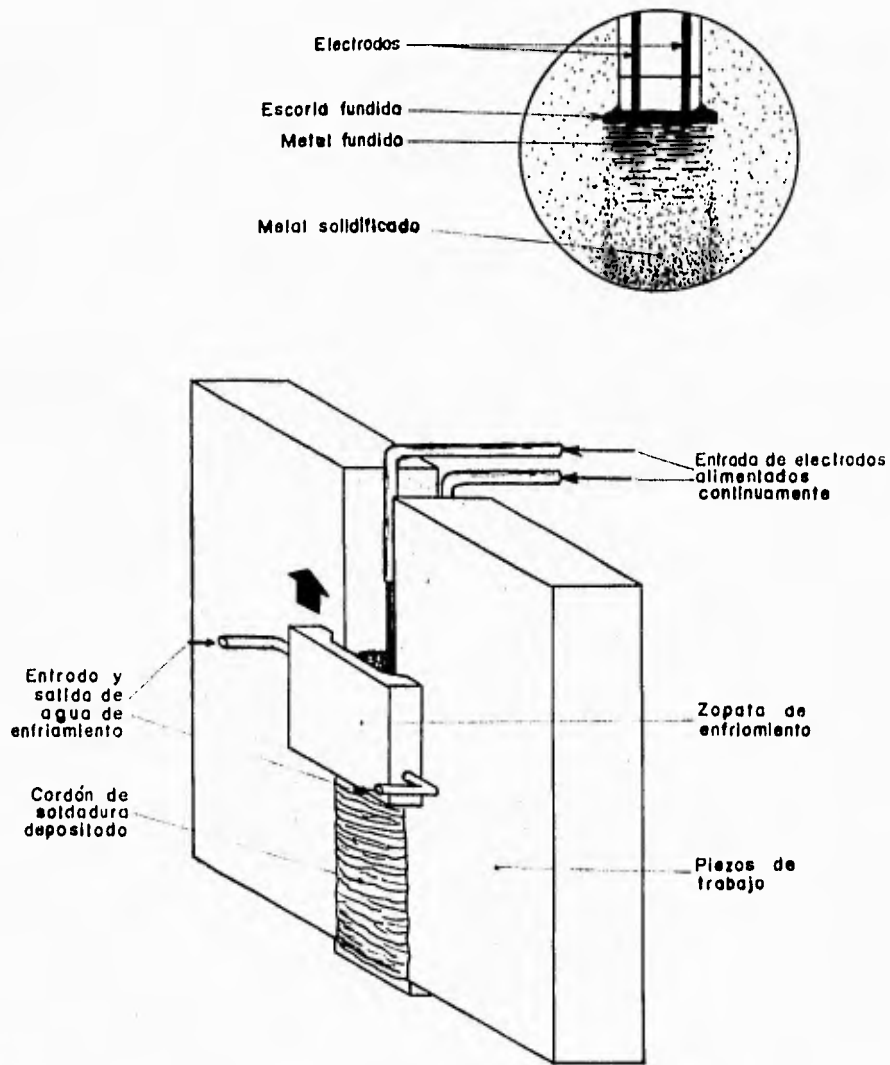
Soldadura por electroescoria (ESW)
